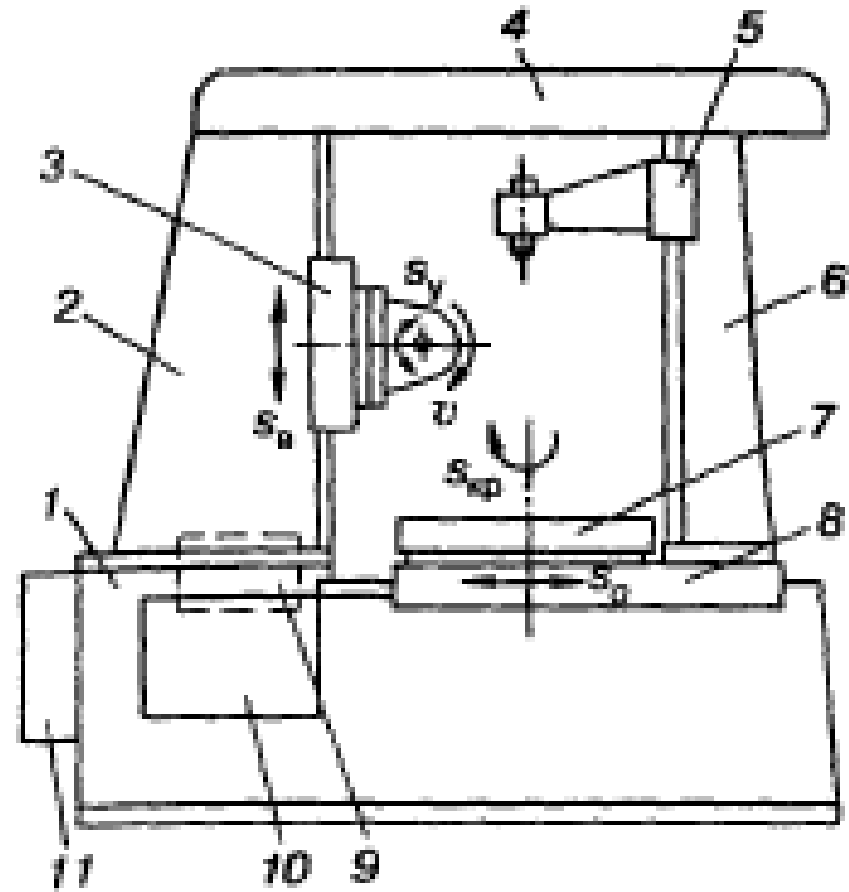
Загальний вигляд зубофрезерного верстата
